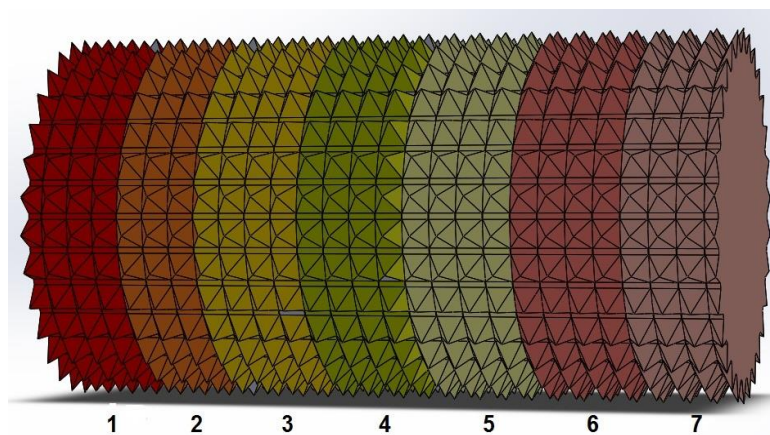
Disposición de soldaduras en la 1° maza superior
